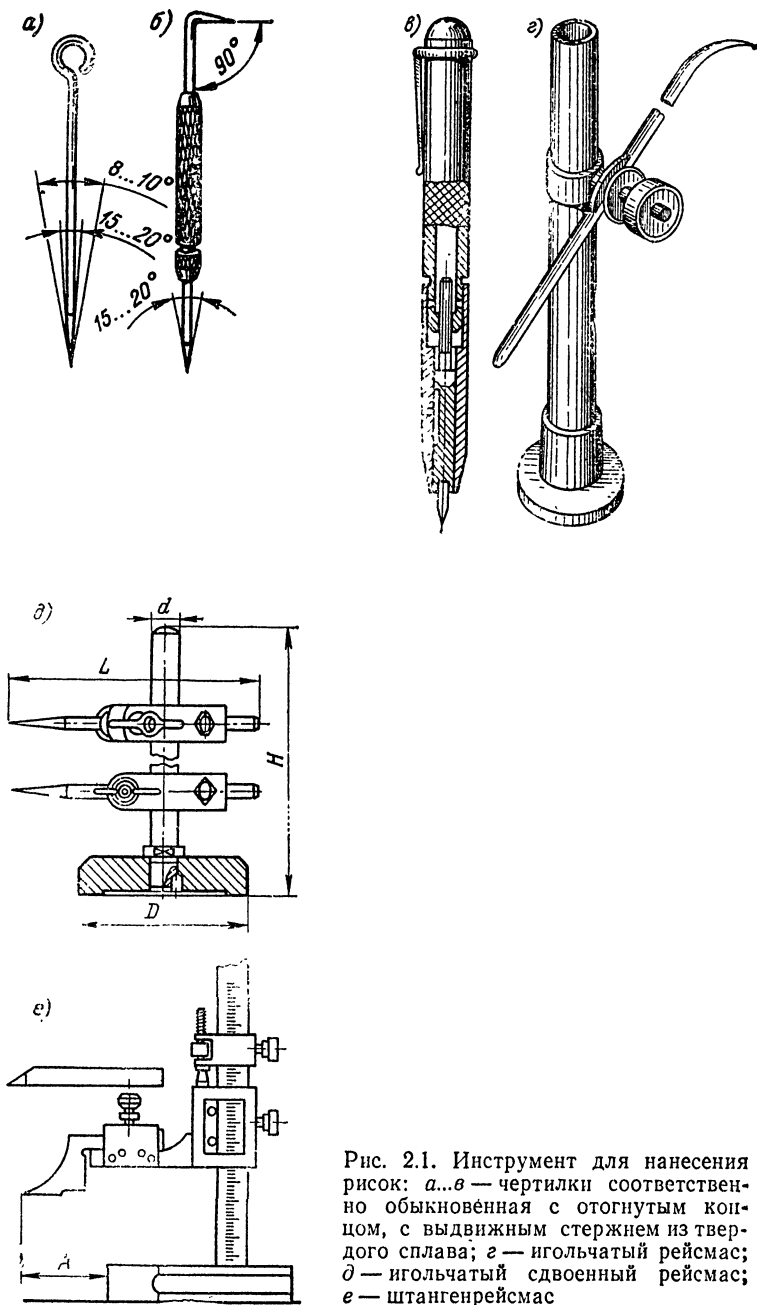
Инструмент для нанесения риска: а...в — чертилки соответственно обыкновенная с отогнутым концом, с выдвигаемым стержнем из твердого сплава; г — игольчатый рейсмас; д — игольчатый двоянный рейсмас; е — штангенрейсмас
